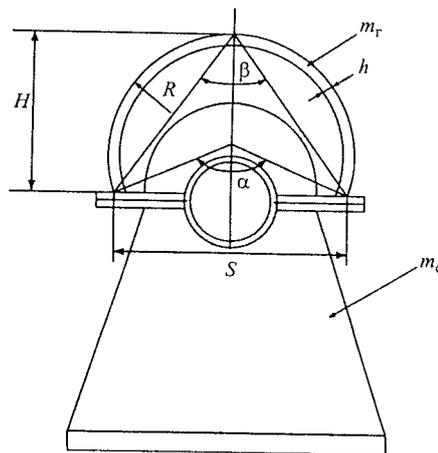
Схема расположения основных элементов виброгасителя на крышке подшипника опоры:
